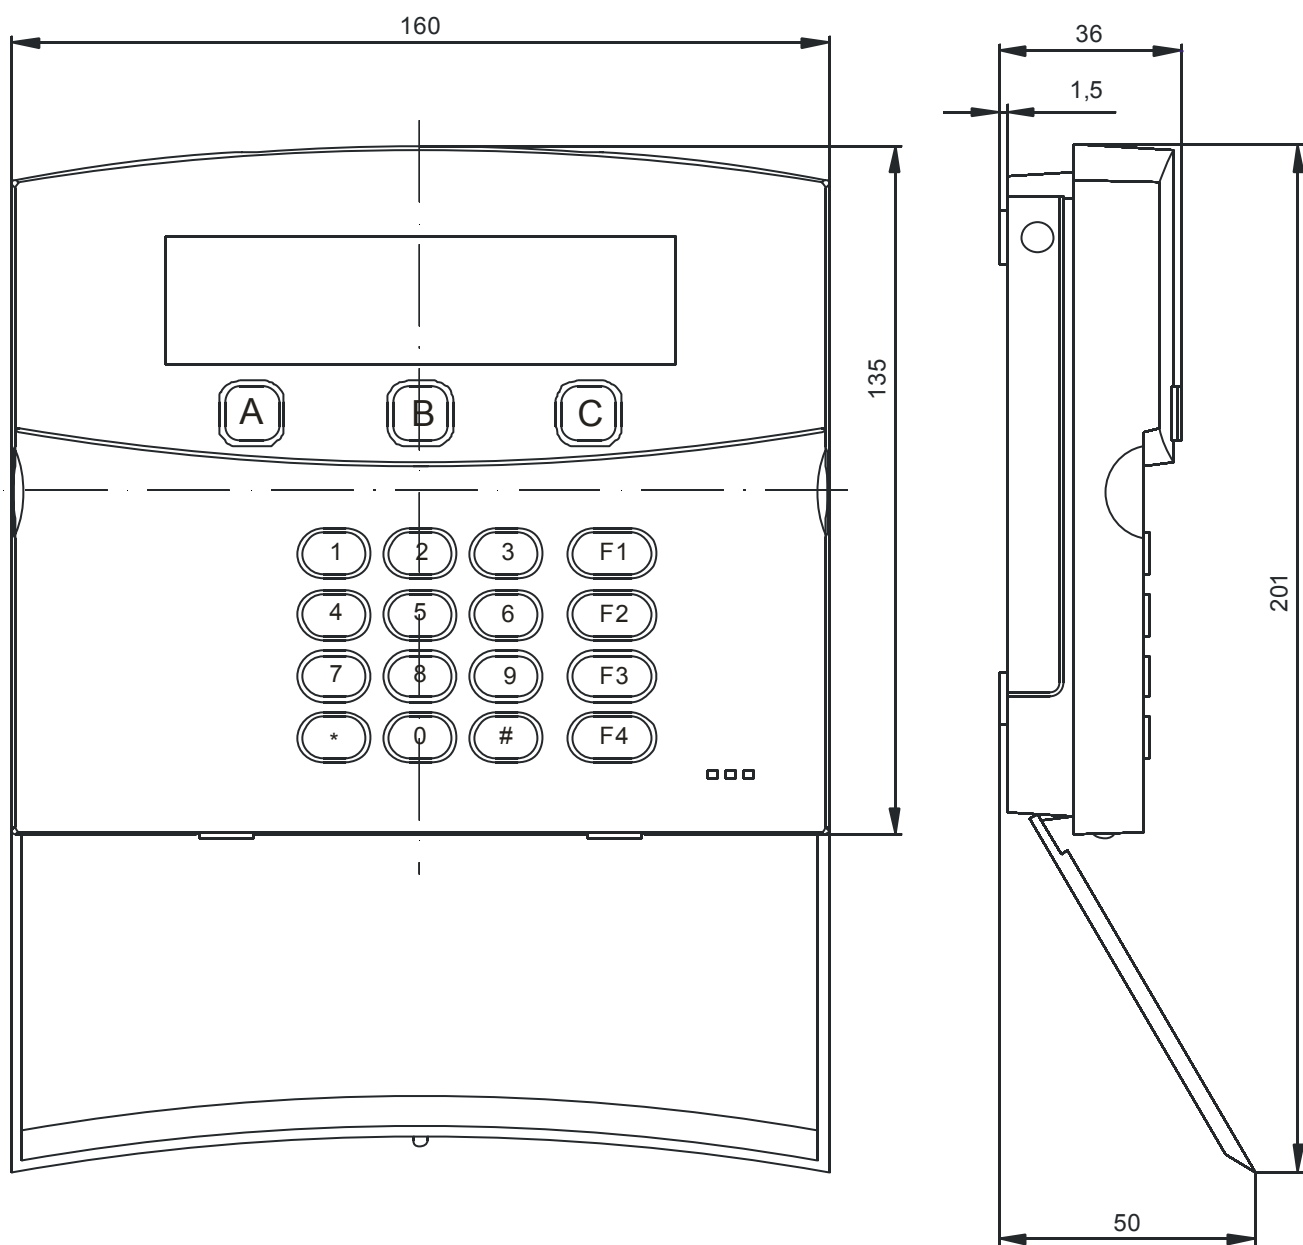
Габаритный чертеж корпуса (крышка откинута).
